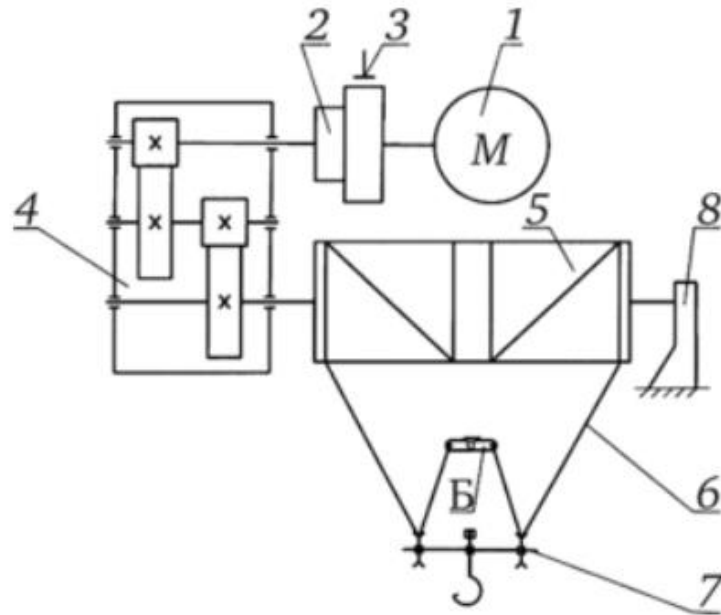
Кінематична схема підйомного механізму баштового крана, де 1 – електродвигун; 2 – пружна муфта; 3 – гальма; 4 – редуктор; 5 – барабан; 6 – канат; 7 – гакова підвіска; 8 – кріпильна опора барабана.
